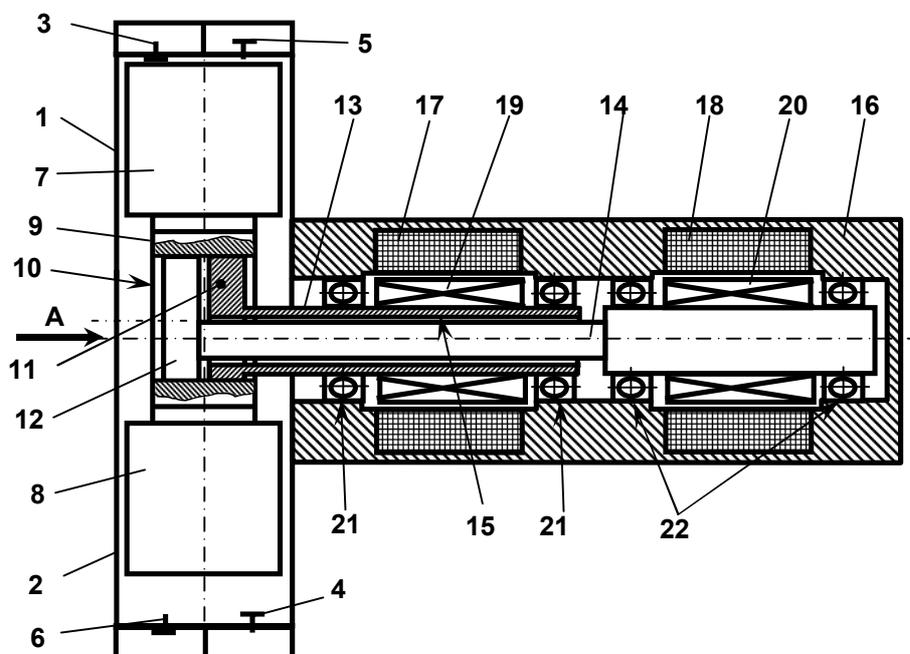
Схема продольного сечения конструкции оппозитного компрессора с совмещенными электродвигателями
